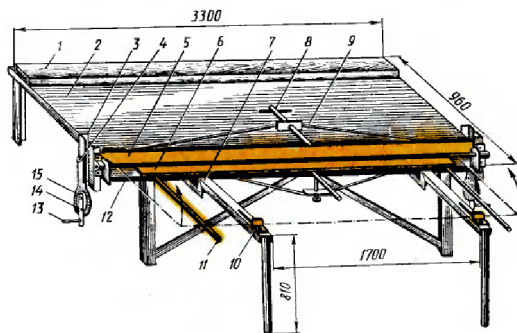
Большой фальцегибочный станок конструкции И. П. Прохорова: 1 — упорная рейка, 2 — верстак, 3 — опорная стойка, 4 — продольная трубчатая ось, 5, 6, 12 — прижимной, гибочный и неподвижный угольники, 7 — кронштейн, 8 — нажимной винт, 9 — растяжка, 10 — упоры, 11 — рычаг, 13 — рукоятка, 14 — эксцентрик, 15 — шатун
